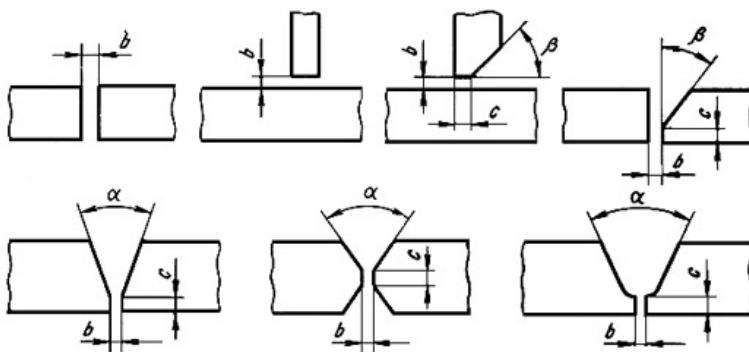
7. Конструктивные элементы разделки кромок и сборки кромок под сварку
